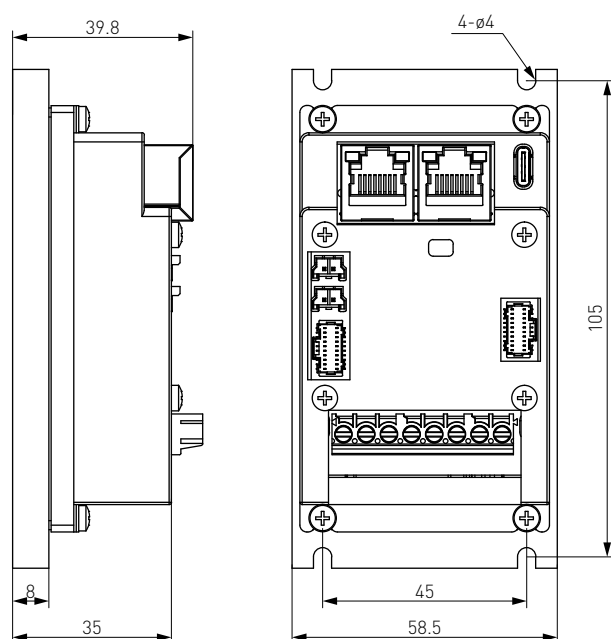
Габаритный чертеж серводрайверов ELD3-EC7001/7005BH.
